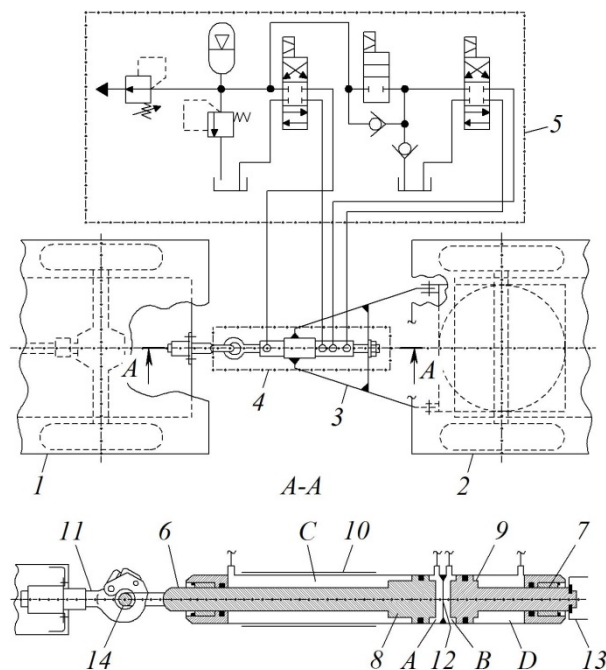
Конструкция дышла сцепного устройства автопоезда: 1 – лесовозный тягач; 2 – прицепное звено; 3 – дышло сцепного устройства; 4 – последовательно соединенные торцами два гидроцилиндра двухстороннего действия; 5 – гидропривод; A, B и C, D – поршневые и штоковые полости гидроцилиндров двухстороннего действия; 6, 7 и 8, 9 – штоки и поршни гидроцилиндров двухстороннего действия; 10 – корпус дышла; 11 – крюк; 12 – герметичная перегородка; 13 – поперечина дышла; 14 – присоединительное кольцо
